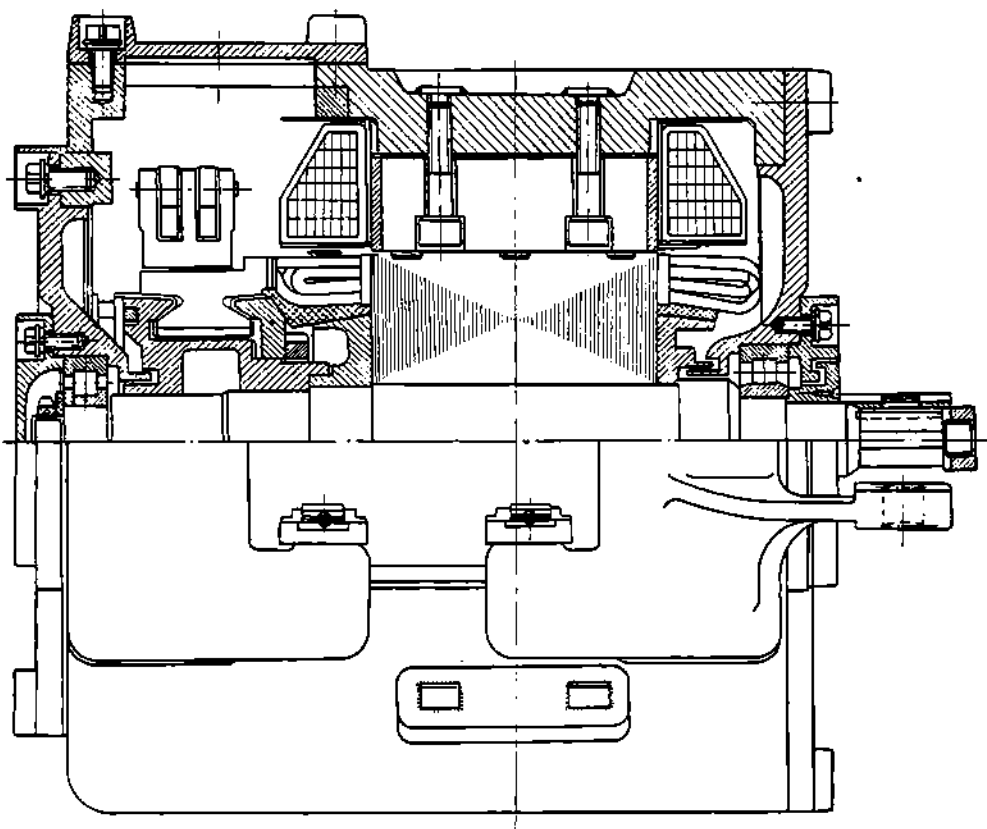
Secțiune prin motorul tip SSTA 4,5-72.
